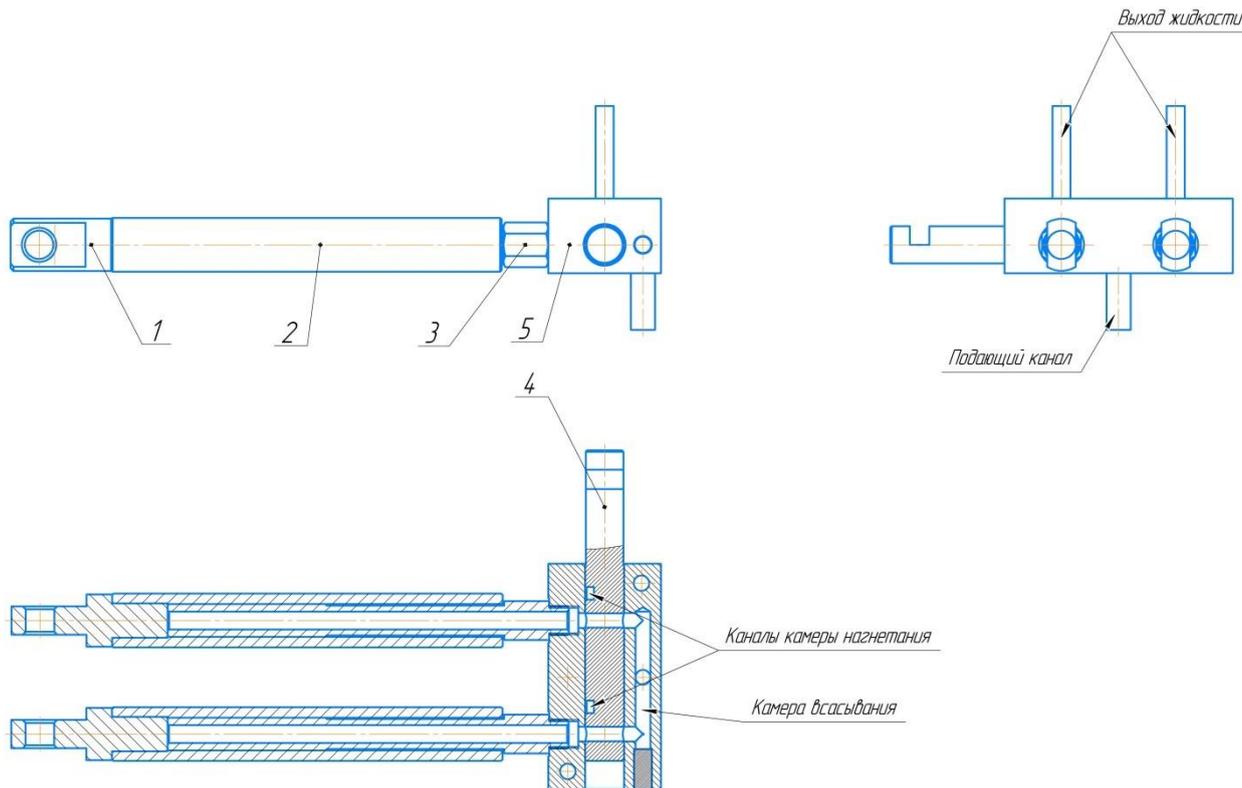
сборочная схема дозатора, 5 мл.
